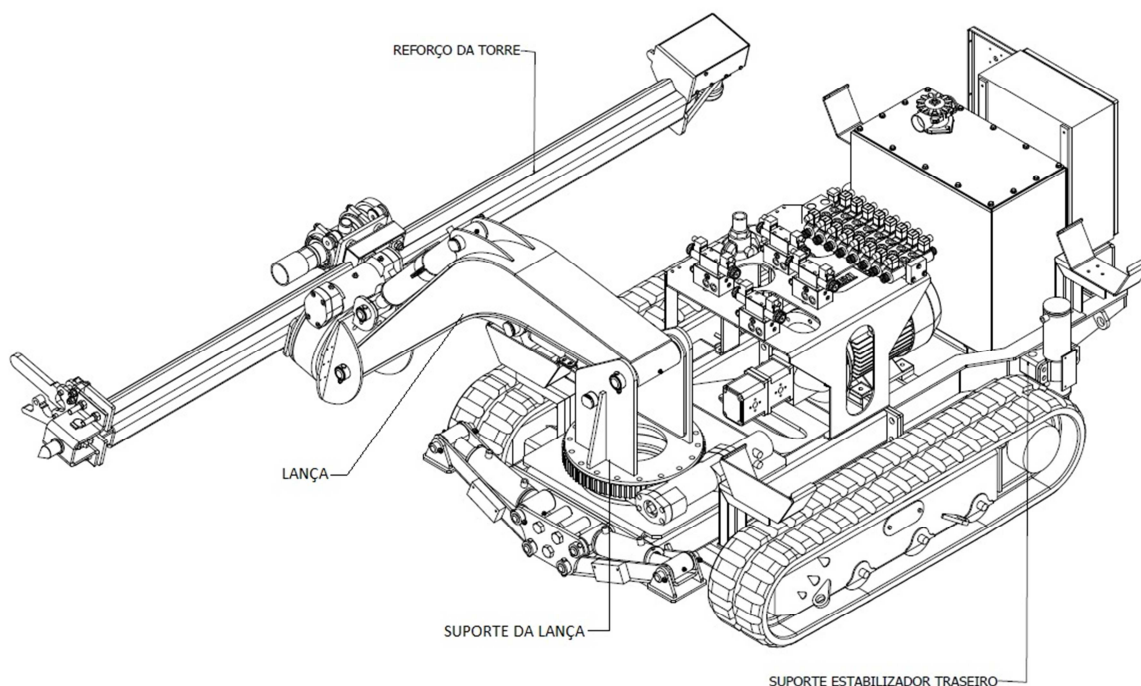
Indicação das principais soldaduras dimensionadas (continuação)
